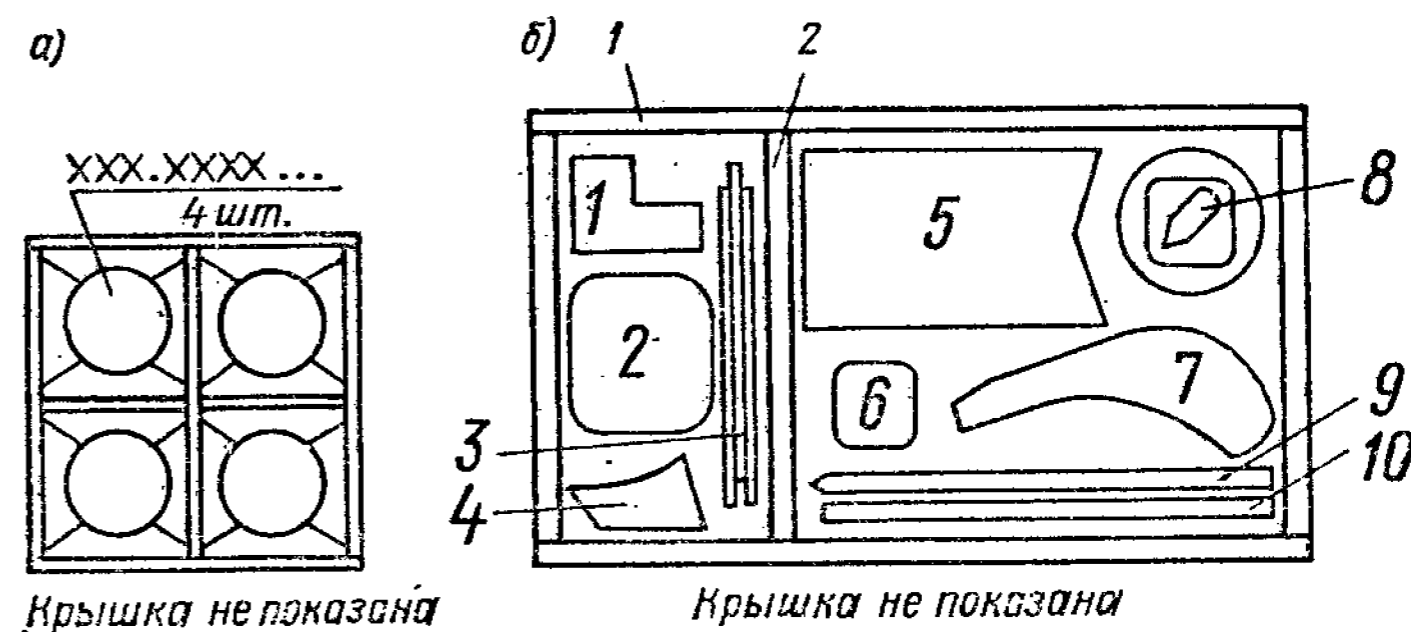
Способы указания обозначений и наименований упаковываемых изделий на сборочных чертежах упаковки
